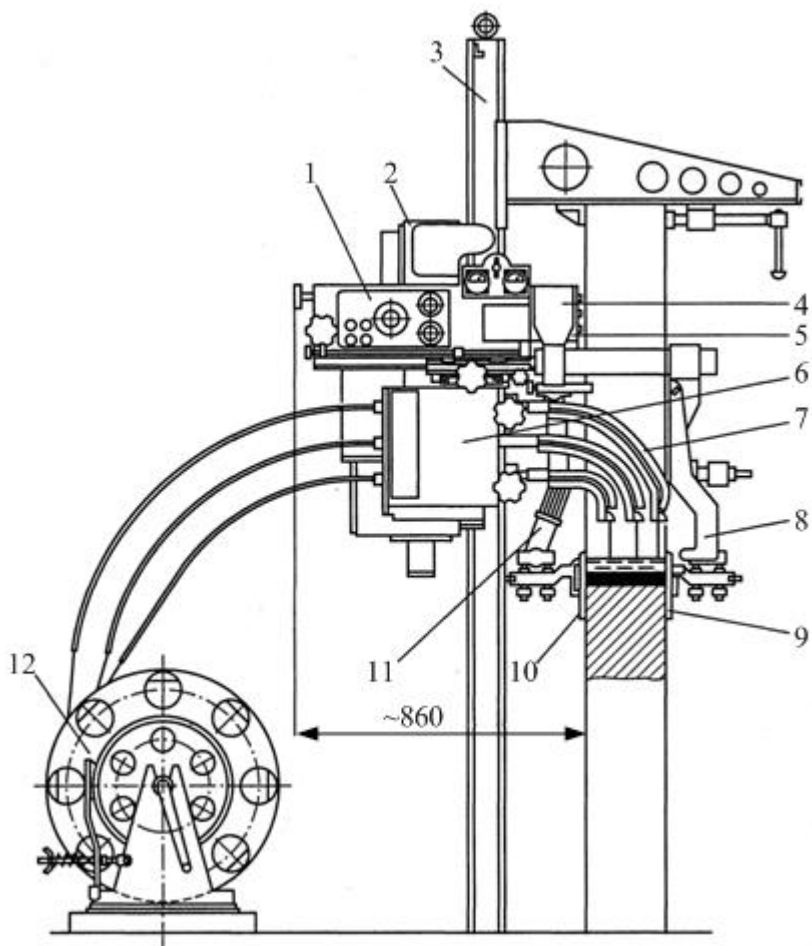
Схема аппарата А-535 рельсового типа для электрошлаковой сварки прямолинейных стыков:
